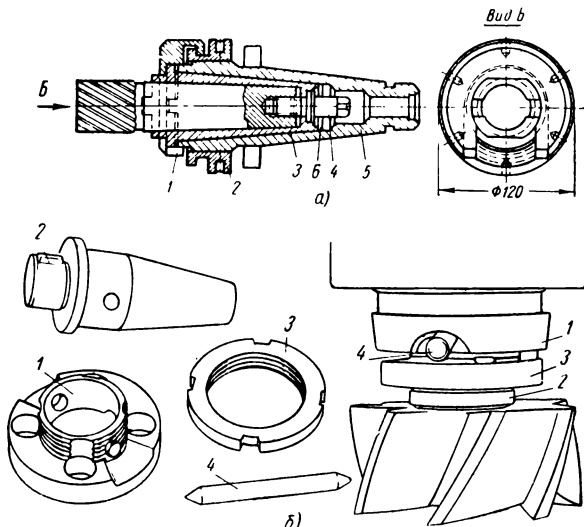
Быстродействующие патроны для закрепления концевых фрез:
